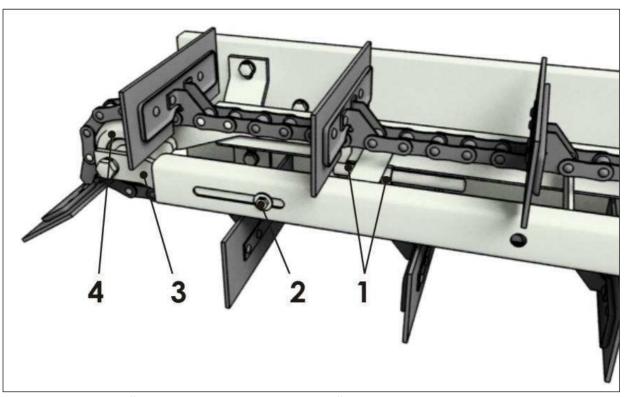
Регулировка натяжения скребковой цепи загрузочного транспортера
